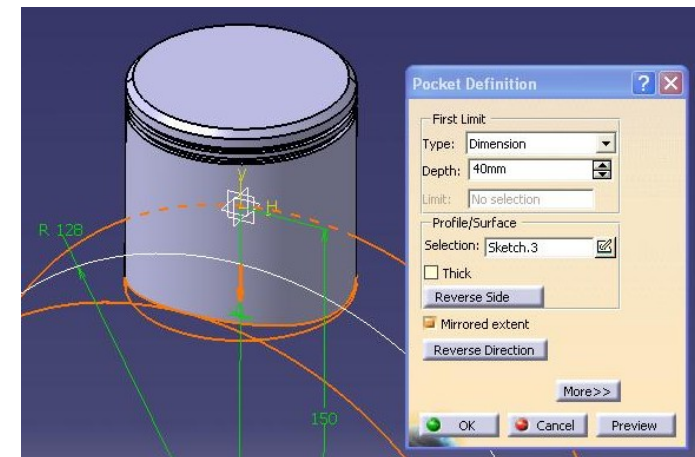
Skica kružnice spodní radiální plochy pístu
